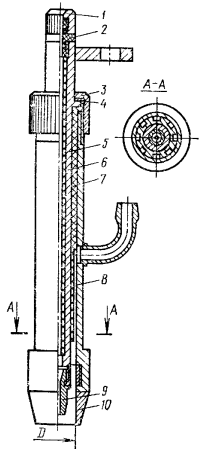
Сварочная горелка типа ГНА-160:
